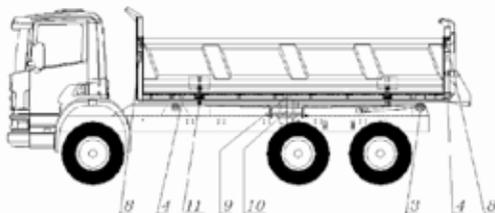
Точки смазки самосвала с трёхсторонней разгрузкой
